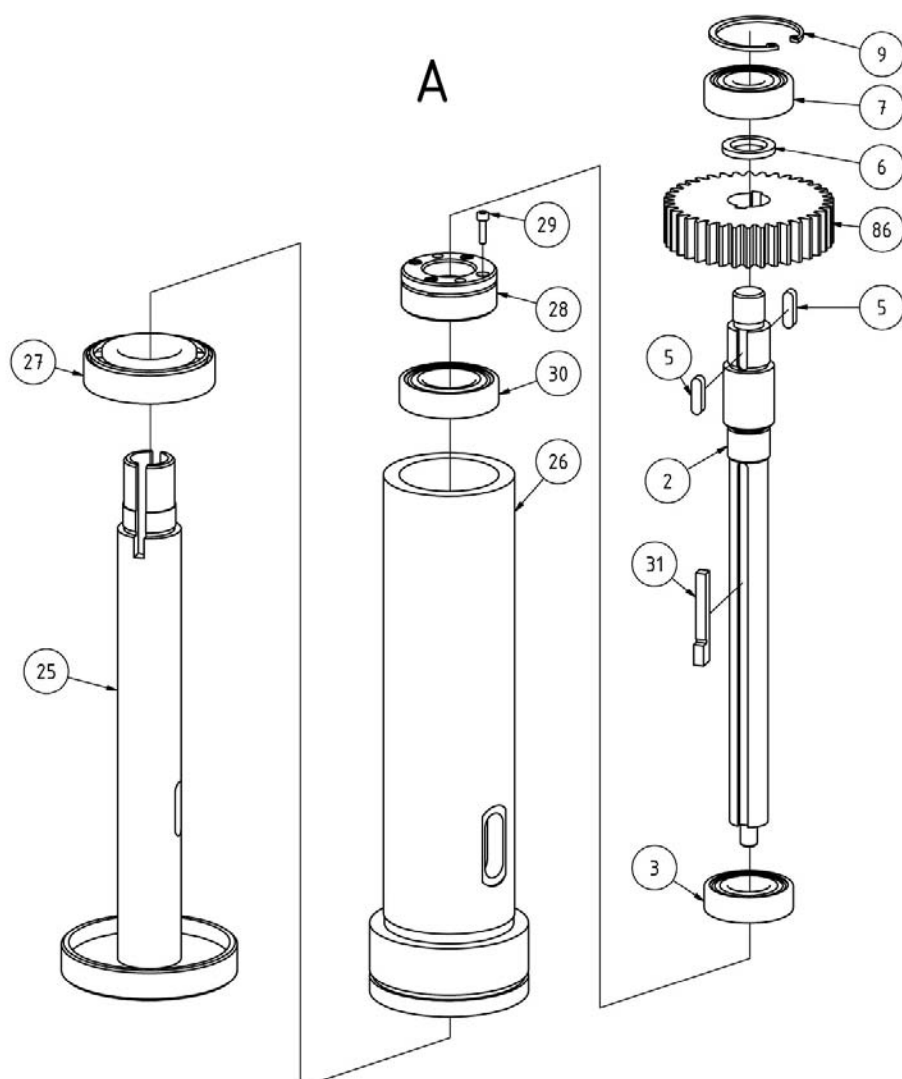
Bohrkopf 1 von 6- Cabezal taladrador 1 de 6
